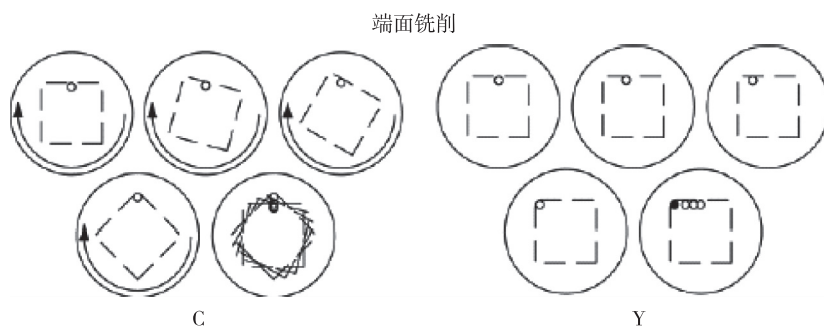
端面铣削 C 轴转动补偿 Y 轴移动
